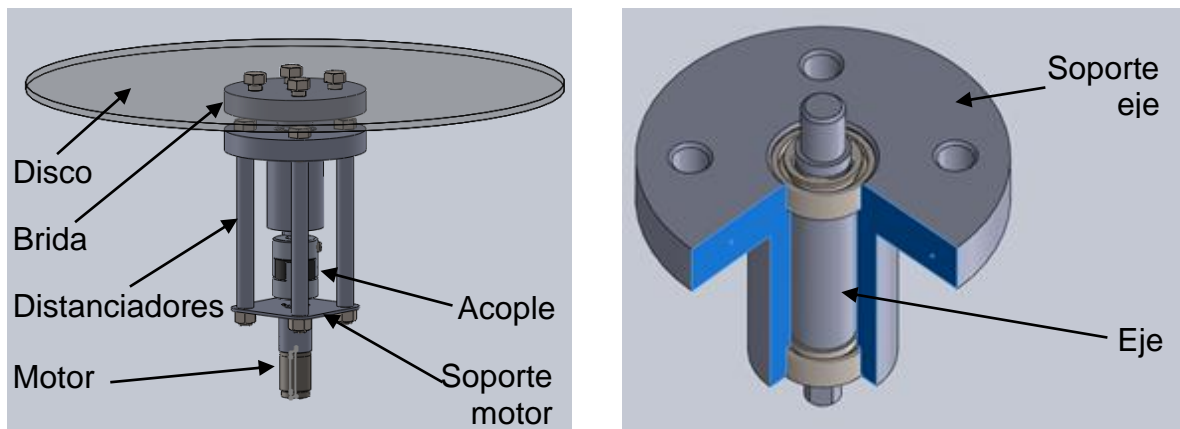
Disco y sistema de giro – Plano ref. PI-119-00-00
